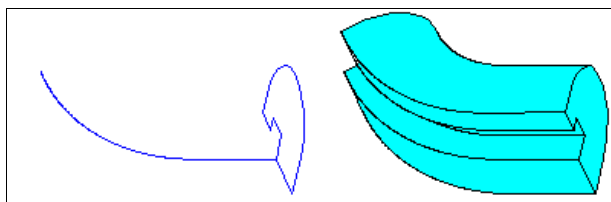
Эскиз и элемент, образованный «Кинематической операцией»
